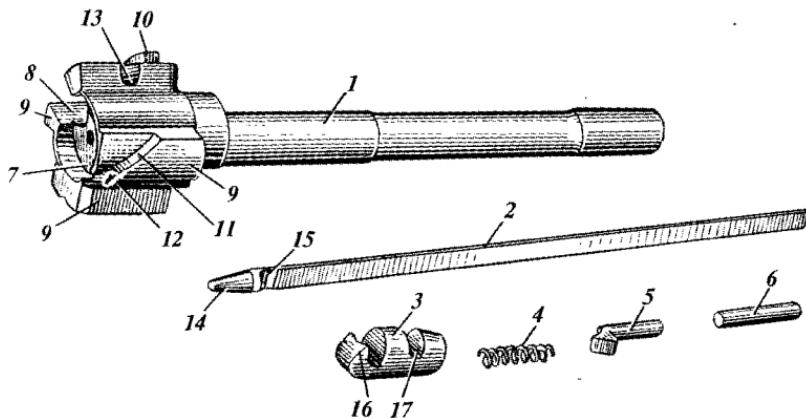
Затвор СВД-63: 1 — оствол затвора; 3 — ударник; 3 — выбрасыватель; 4 — пружина выбрасывателя; 5 — ось выбрасывателя б- шпилька ударника; 7 — вырез для дна гильзы; 8 — вырез для выбрасывателя; 9 — боевые выступы; 10 — ведущий выступ; 11 — скос; 12 — продольный паз для отражательного выступа; 13 — отверстие для оси выбрасывателя; 14 — боек ударника; 15 — уступ для шпильки; 16 — зацеп выбрасывателя; 17 — вырез для оси.
